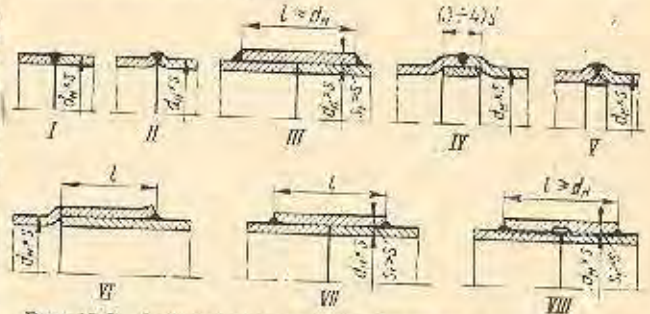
Основные типовые конструкции неразъемного соединения труб между собой:
